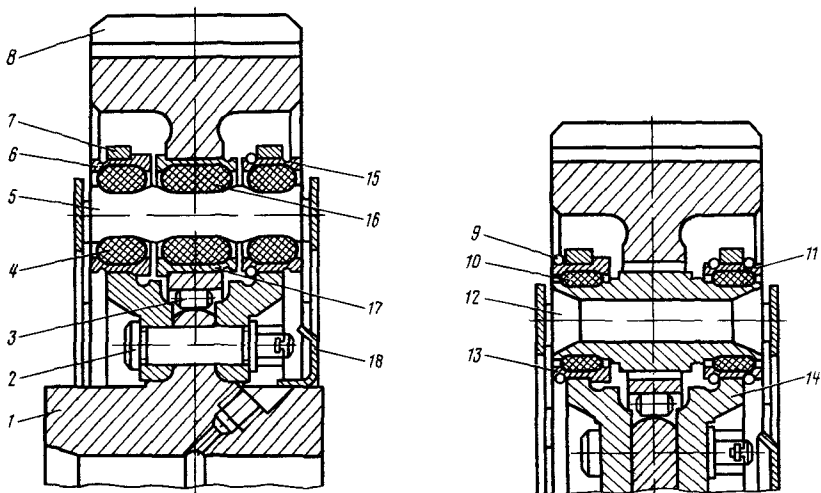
Упругое зубчатое колесо тягового редуктора:
